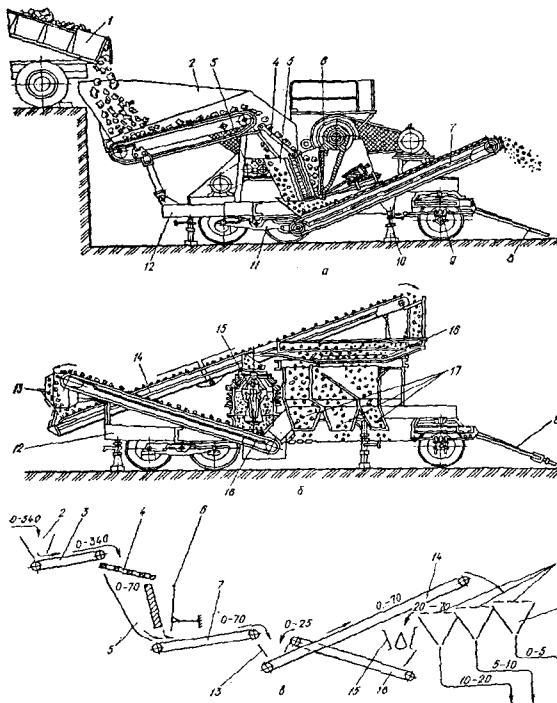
Передвижная дробильно-сортировочная установка средней производительности: а – агрегат крупного дробления; б – агрегат мелкого дробления; в – схема работы установки; 1 – погрузчик; 2, 17 – бункеры; 3 – пластинчатый питатель; 4 – колосниковая решетка; 5 – лоток; 6 – щековая дробилка; 7, 14, 18 – конвейеры; 8 – прицепное устройство; 9 – передняя тележка; 10 – домкрат; 11 – задняя тележка; 12 – рама; 13 – приемная воронка; 15 – конусная дробилка; 16 – грохот.
